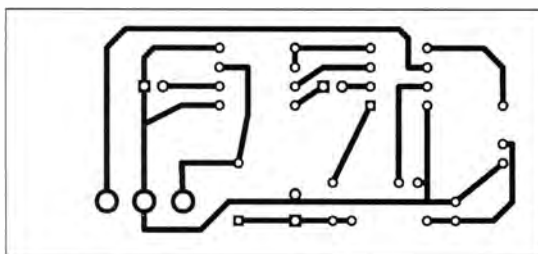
Layout der Lichtschranke; Abmessungen 33 mm x 72,3 mm, M 1:1
